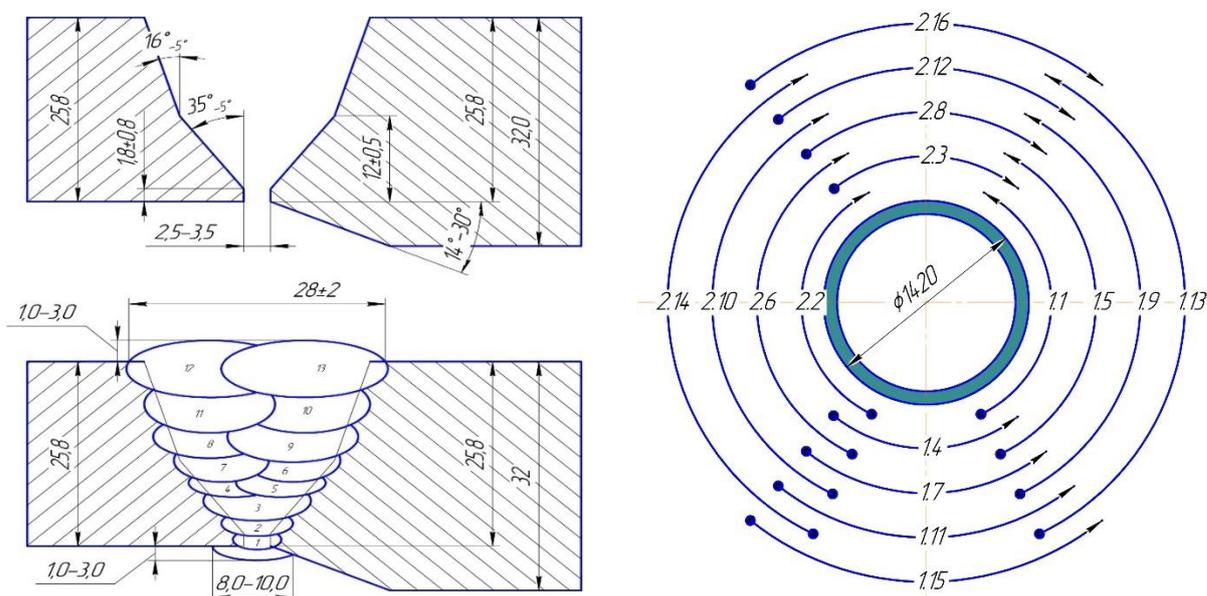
Геометрическая конструкция стыкового соединения разнотолщинных соединений и направление сварки двумя сварщиками.
